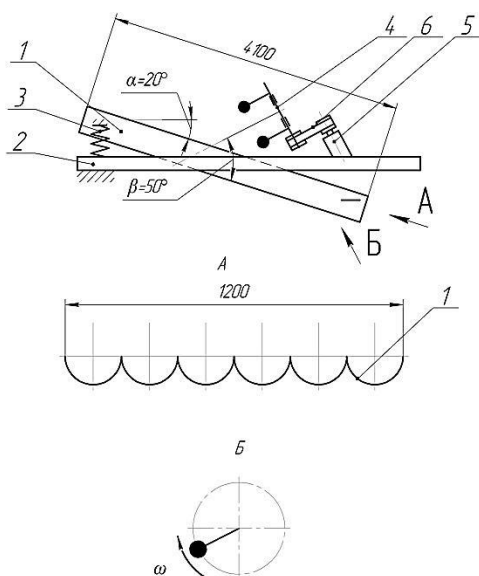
Динамічна схема установки ОЖВ для віброзміцнювальної обробки сирих окатишів: 1 – орган робочий; 2 – рама опорна; 3 – амортизатори; 4 – вібратор дебалансний; 5 – електродвигун; 6 – передача клинопасова
